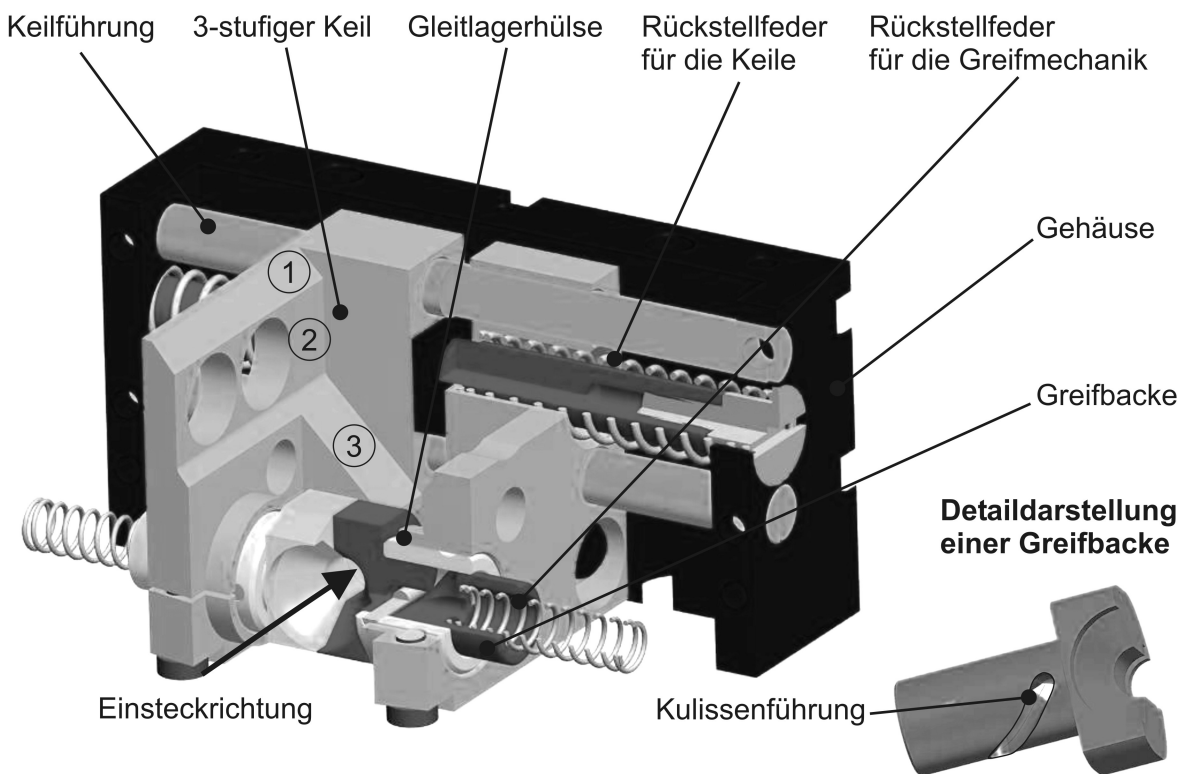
Drehmechanismus zur Orientierung und zum Einstecken der Bolzen in den Bolzenhalter des Schweißkopfes
